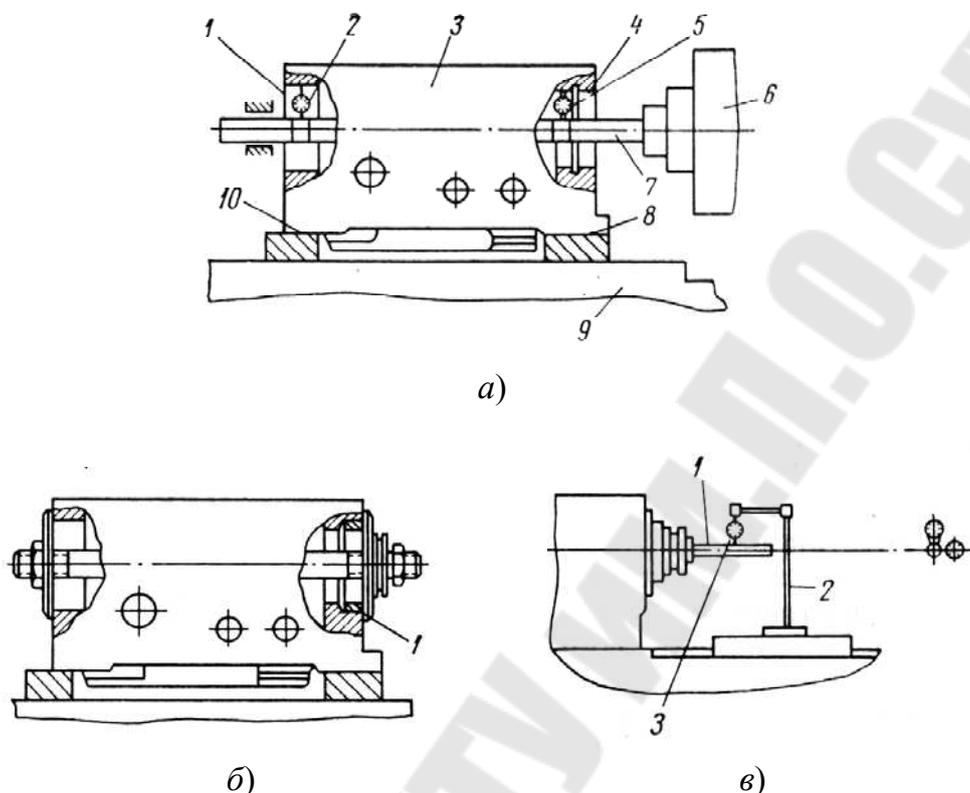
Схемы ремонта корпуса передней бабки
